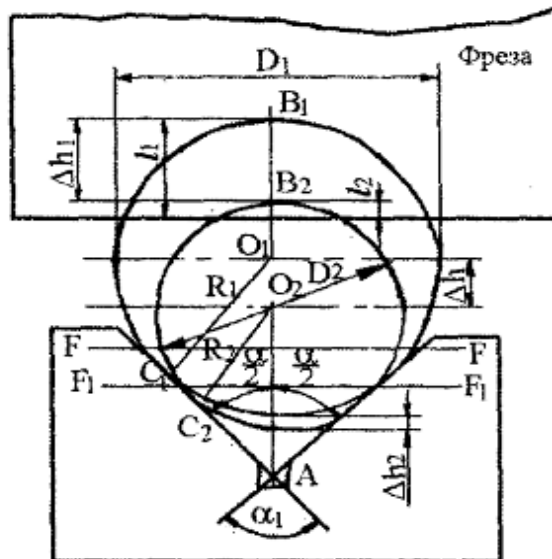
Схема для визначення похибок базування валів при їх встановленні циліндричною поверхнею на призму
